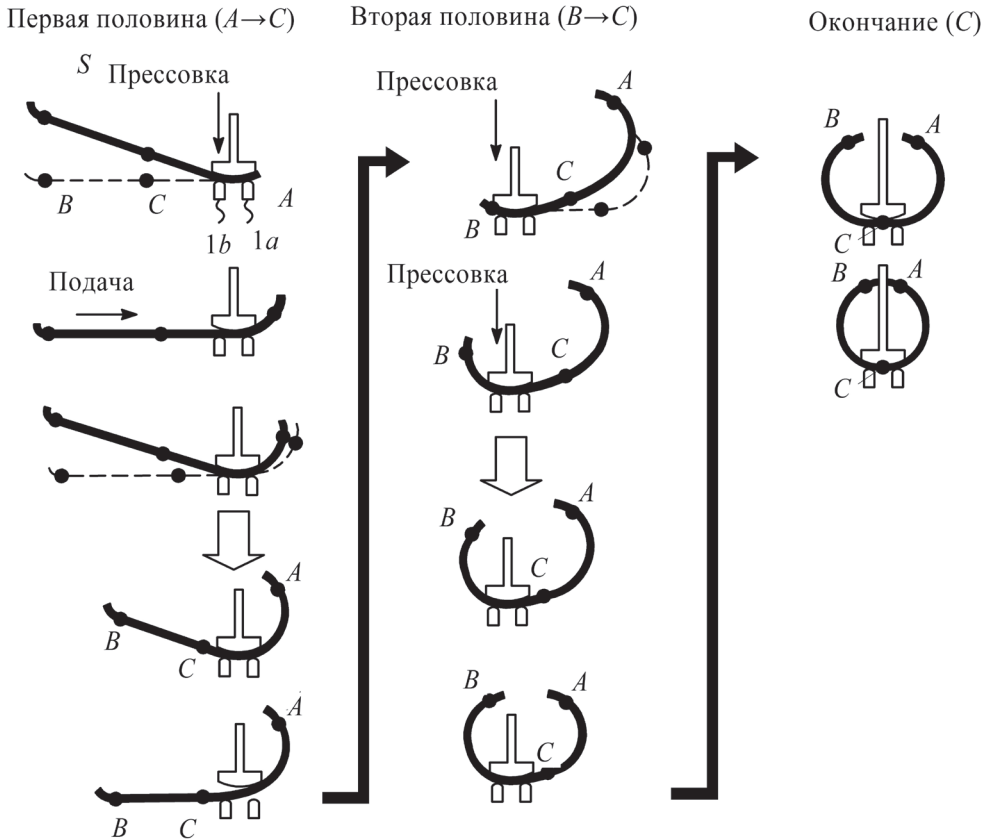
Схема пошаговой формовки трубной заготовки узкими бойками
